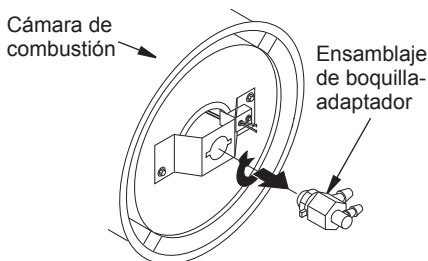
Desmontaje del ensamblaje de la boquilla-adaptador
